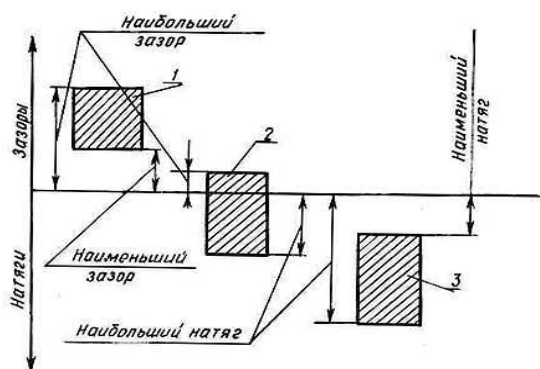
Схема полей допусков для посадок с зазором, натягом
